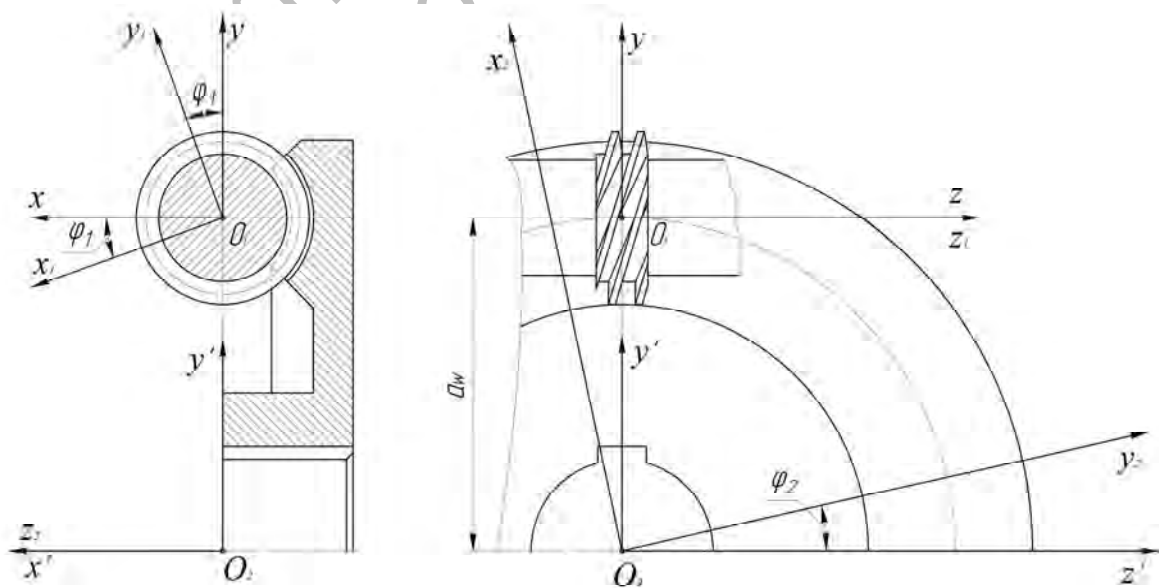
Схема зацепления архимедова червяка с зубьями венца колеса двухвенцовой червячной передачи
